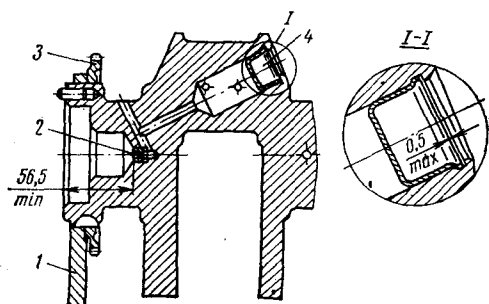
Установка заглушки и ввертыша в коленчатый вал:
